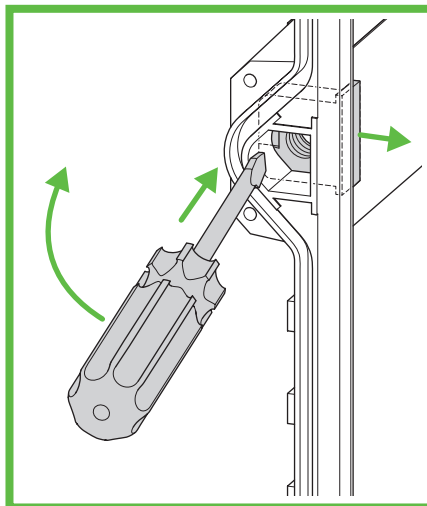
Demontage Gewindeeinschübe GEOS 4050
